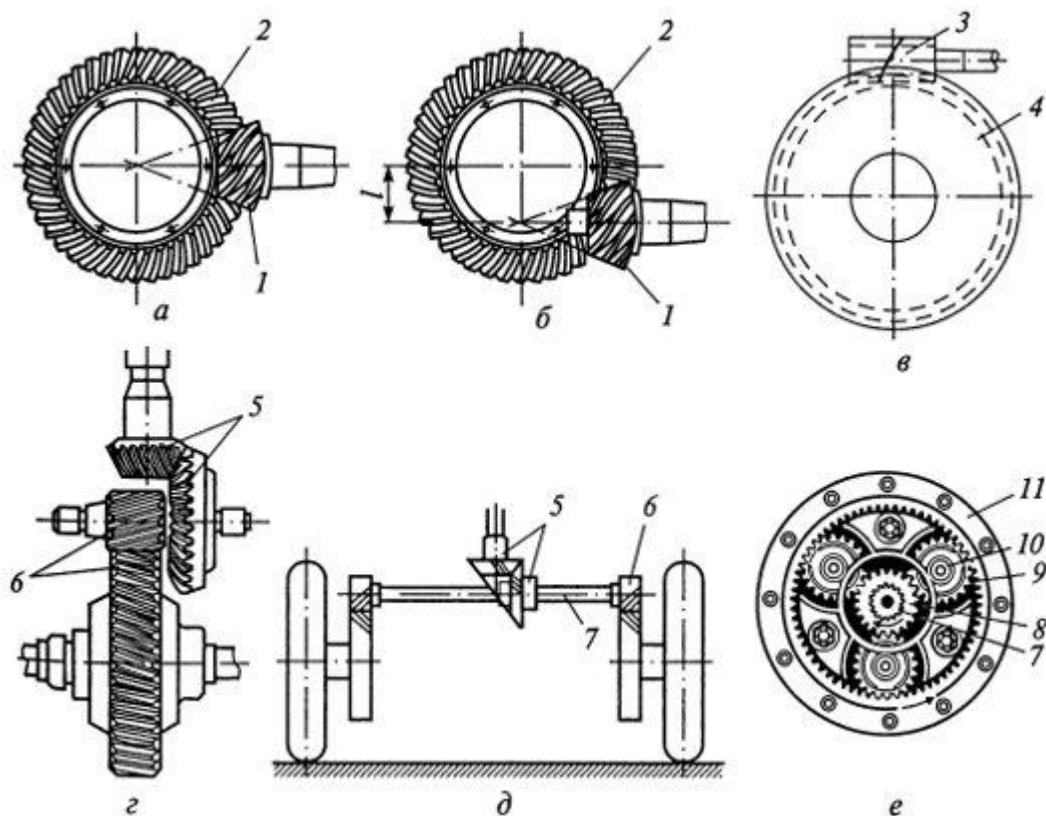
Главные передачи: *а, б, в* – одинарные; *г, д* – двойные; *е* – редуктор; 1 – шестерня; 2 – ведомое зубчатое колесо; 3 – червяк; 4 – червячная передача; 5 – конические зубчатые колёса; 6 – цилиндрические зубчатые колёса; 7 – полуось; 8 – солнечная шестерня; 9 – сателлит; 10 – ось; 11 – коронная шестерня; *l* – гипоидное смещение
